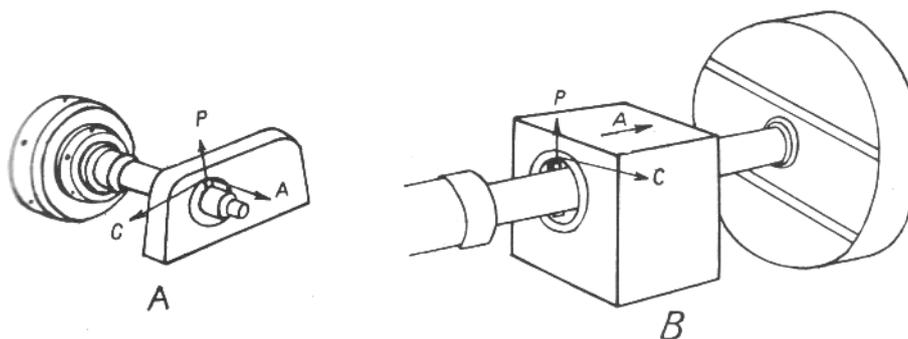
Movimientos de trabajo de la mandrinadora. A) Con avance de la herramienta.
